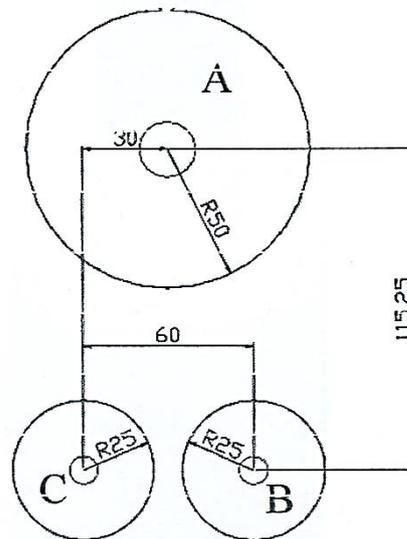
Dimensiones y posición de los moldes: rueda dosificadora y rodillos
